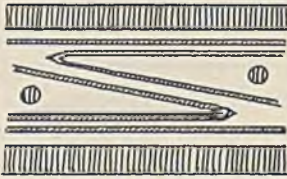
Verschweißen von 6 Blättern zu einem Hohlkörper
